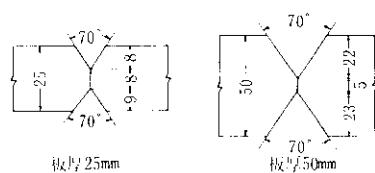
RIVER TEN 62自動溶接継手の開先形状
